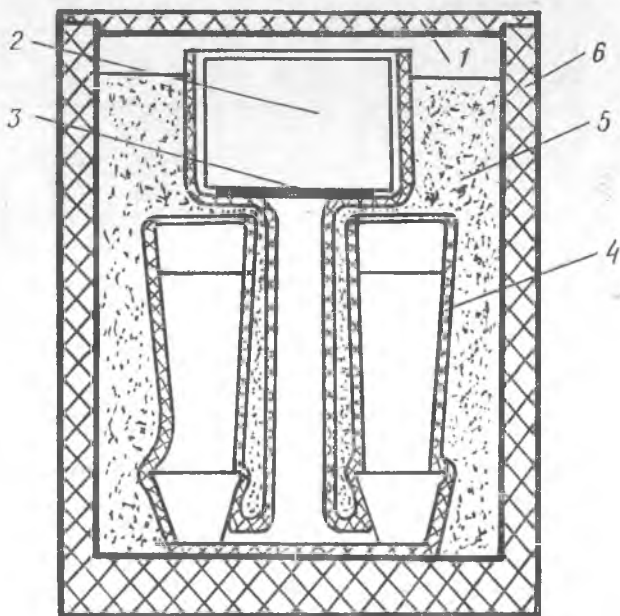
Форма для литья: 1 — графитовая крышка; 2 — шихтовая заготовка; 3 — никелевая фольга; 4 — керамическая оболочка формы лопатки; 5 — засыпка графитовая; 6 — графитовая опока
